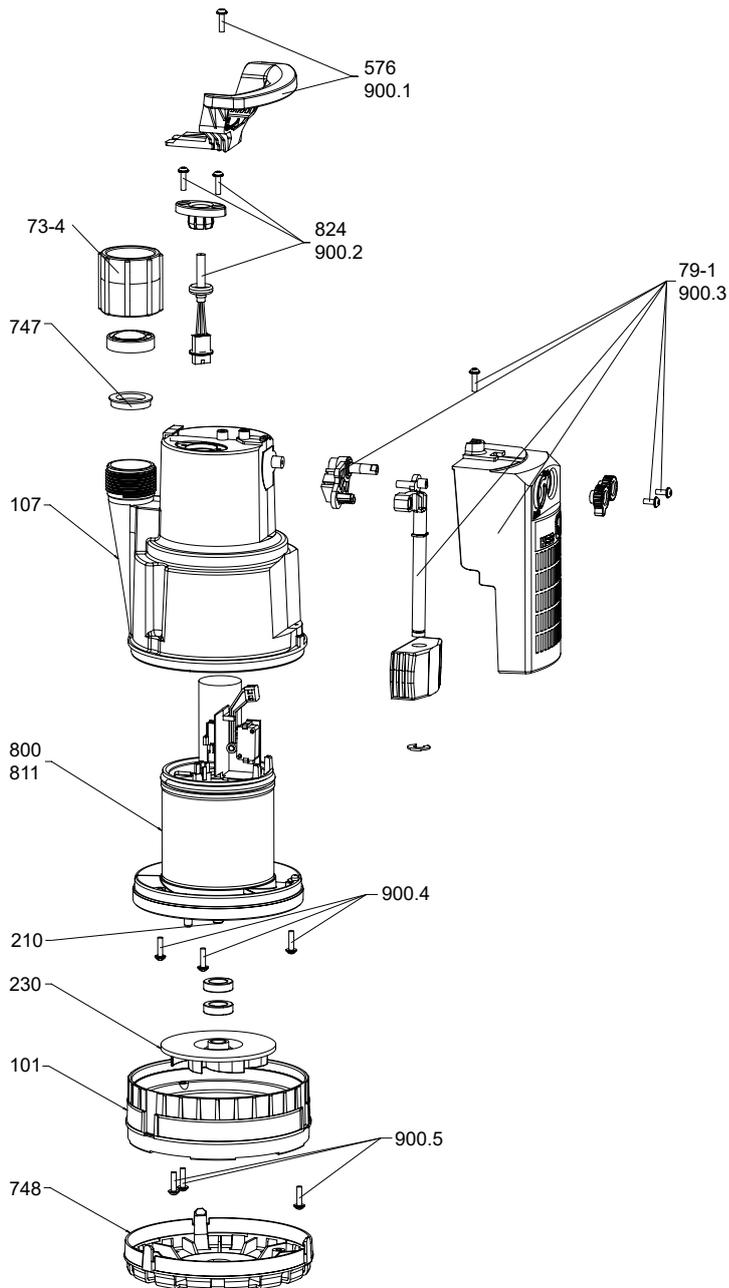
Explosionszeichnung AmaDrainer 301, 303
